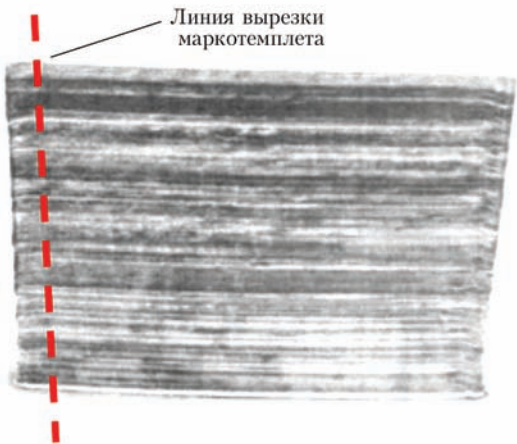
Схема вырезки макротемплета из наплавленной пластины
